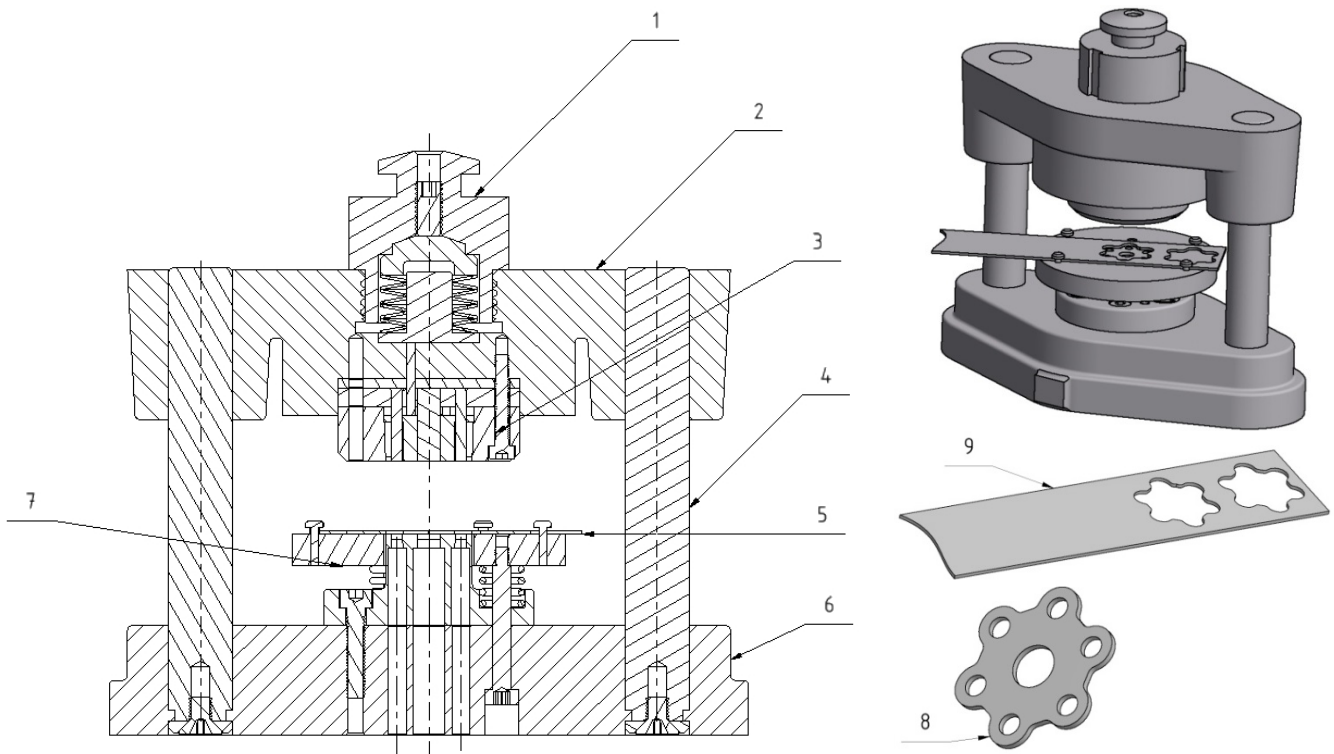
Komplett-Schnittwerkzeug Profilplatte
